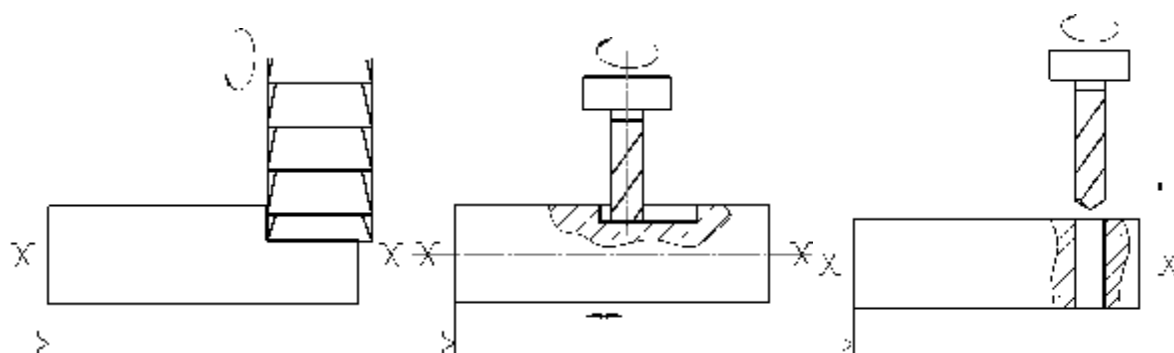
11. Типові схеми обробки циліндричних деталей та схеми їх базування
